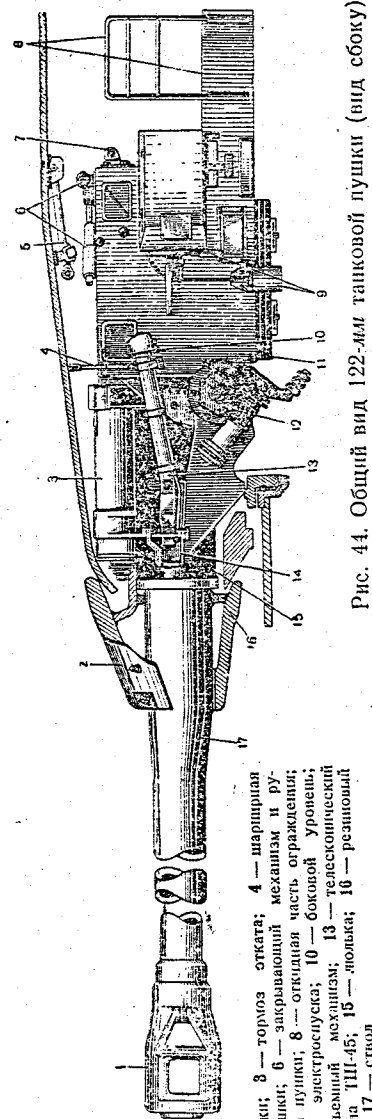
Общий вид 122-мм танковой пушки (вид сбоку):
